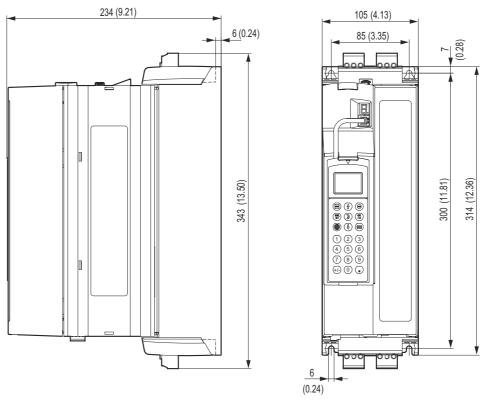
Dimensões MDX61B, tamanho 1, dimensões em mm (in)
